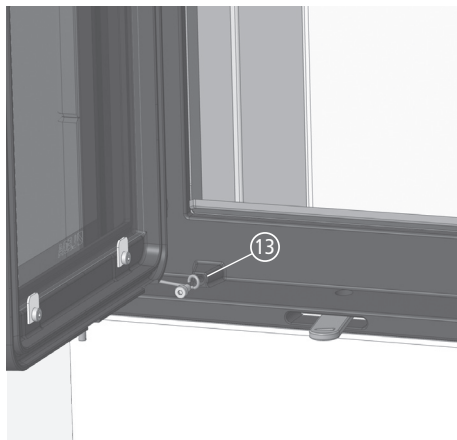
Ovijousen kiristys CORNA:ssa.
